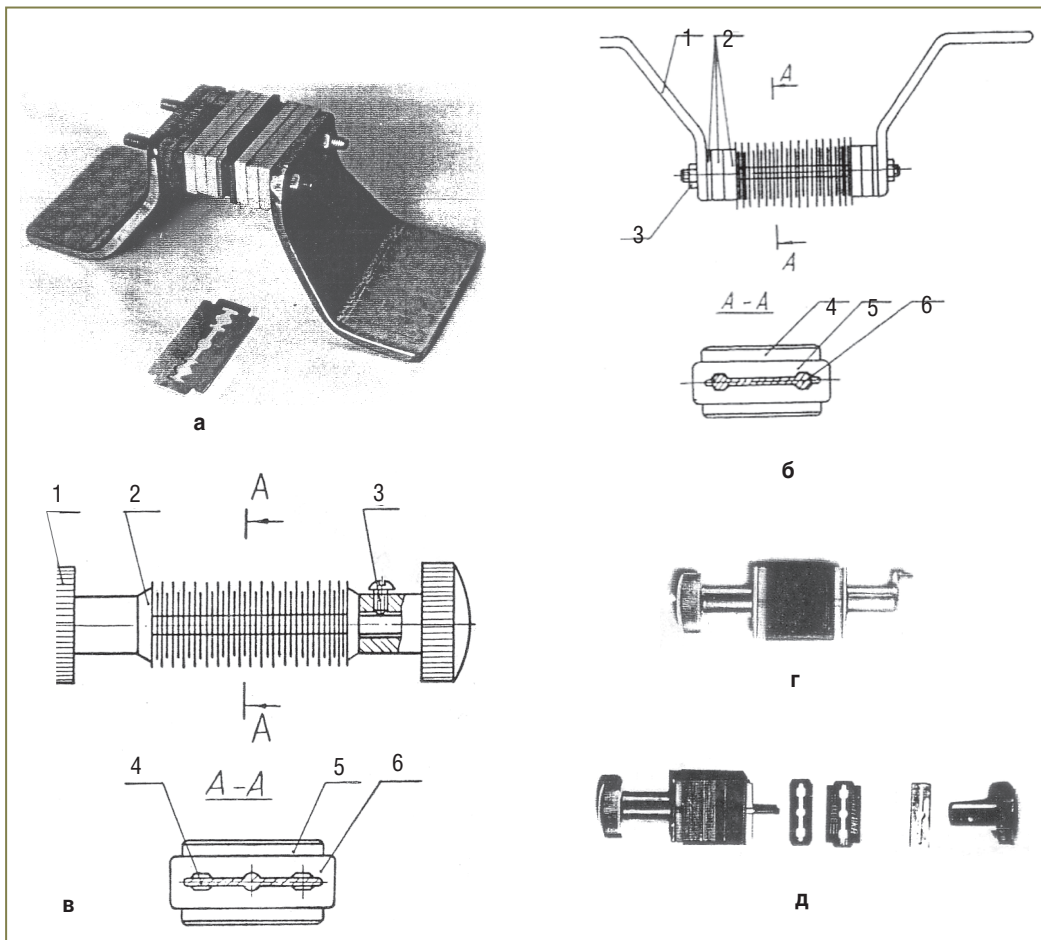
Нож-тандем с набором съемных лезвий безопасной бритвы: а — общий вид; б — 1-й вариант: 1 — ручка; 2 — зажимы; 3 — гайка; 4 — лезвие; 5 — прокладка; 6 — стержень; в — 2-й вариант: 1 — навинчивающаяся сменная ручка; 2 — прижим; 3 — фиксатор; 4 — стержень; 5 — лезвие; 6 — разделительная прокладка-вкладыш; г — опытный образец в сборе, д — в разобранном виде
